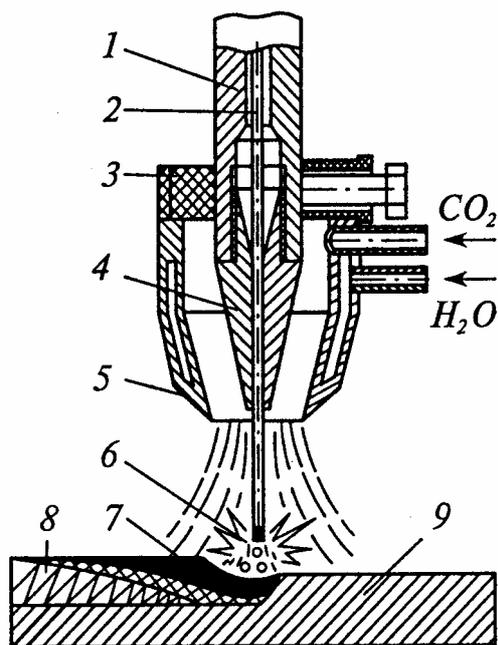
Схема наплавки в среде диоксида углерода: 1 – мундштук; 2 – электродная проволока; 3 – горелка; 4 – наконечник; 5 – сопло горелки; 6 – электрическая дуга; 7 – сварочная ванна; 8 – покрытие; 9 – восстанавливаемая деталь
